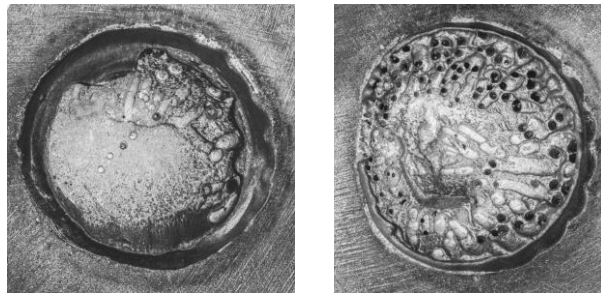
Verschweißung mit einem Porenanteil von 10 bis 25 % (links) und Porenanteil von > 25 % (rechts)
